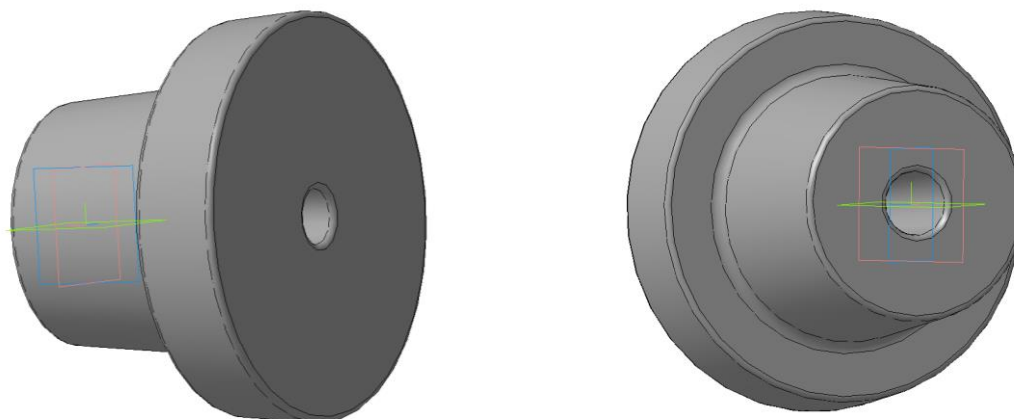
3D- модель заготовки детали «корпус цанги»
